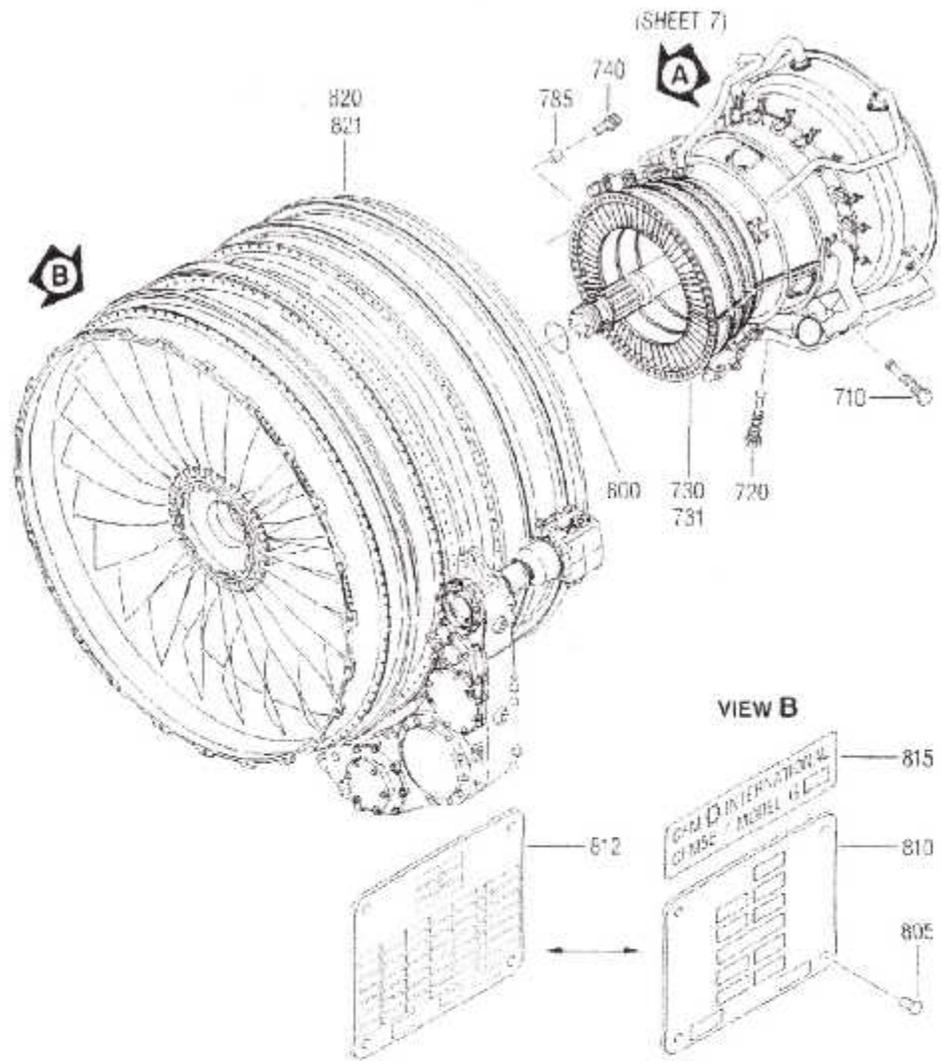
Dépose de la Bague de Retenue du Rotor HPC.
